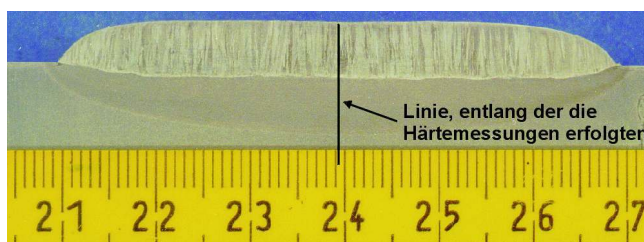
Makroschliff einer RES-Plattierschweißung
